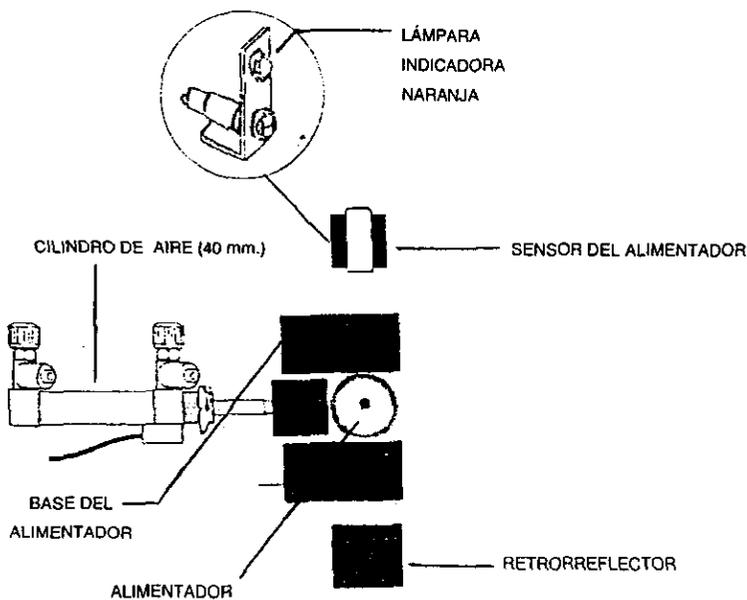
Vista en planta del cilindro, base, tubo alimentador y el sensor de piezas.
